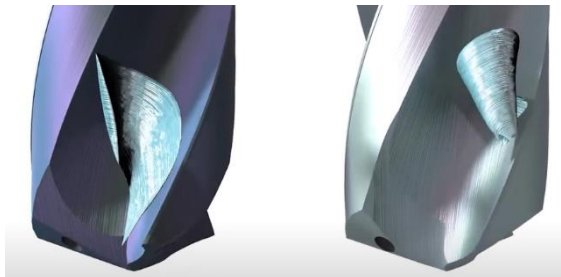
Форма стружки для свердла з трьома канавками звичайної та покращеної конструкції
